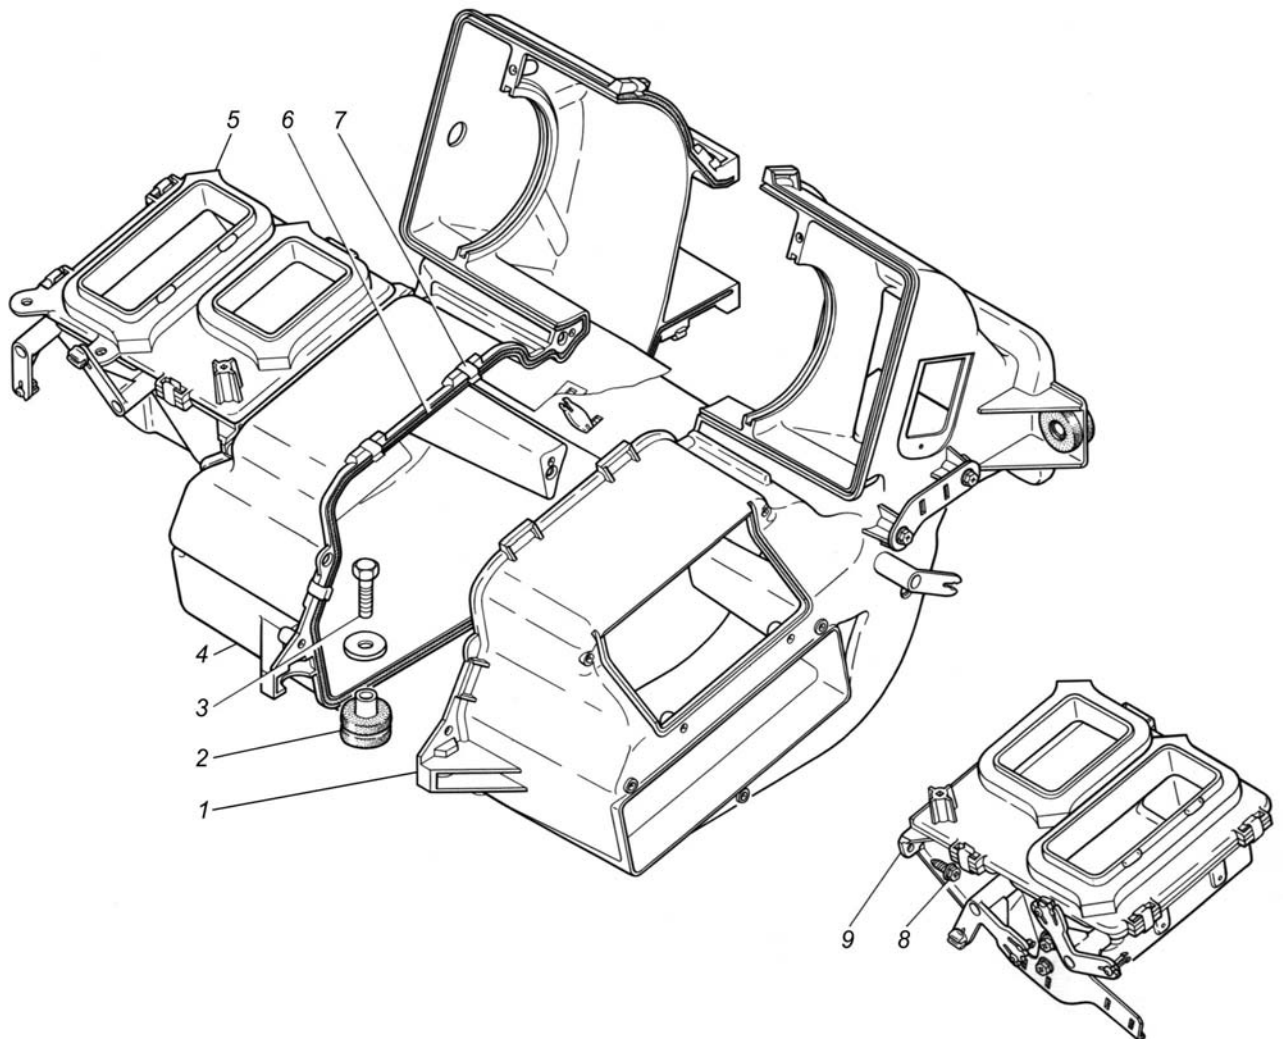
Детали корпуса отопителя: 1 – крышка кожуха ОВУ; 2 – втулка; 3 – болт крепления ОВУ; 4 – кожух ОВУ; 5 – распределитель левый; 6 – прокладка кожуха ОВУ; 7 – скоба; 8 – винт; 9 – распределитель правый
